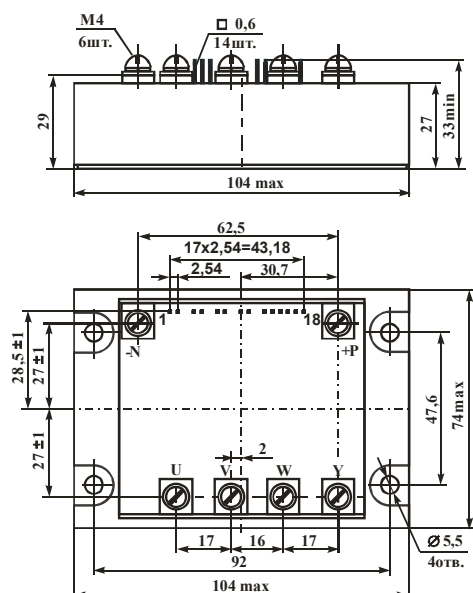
Габаритный чертеж модулей M13B-10-6(12)
